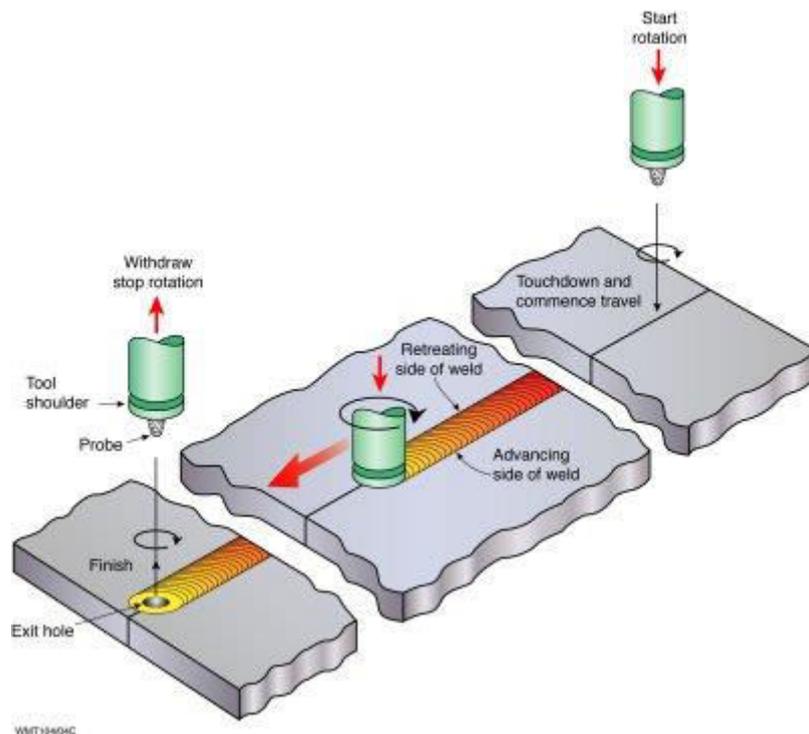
Principe du soudage par friction malaxage.
